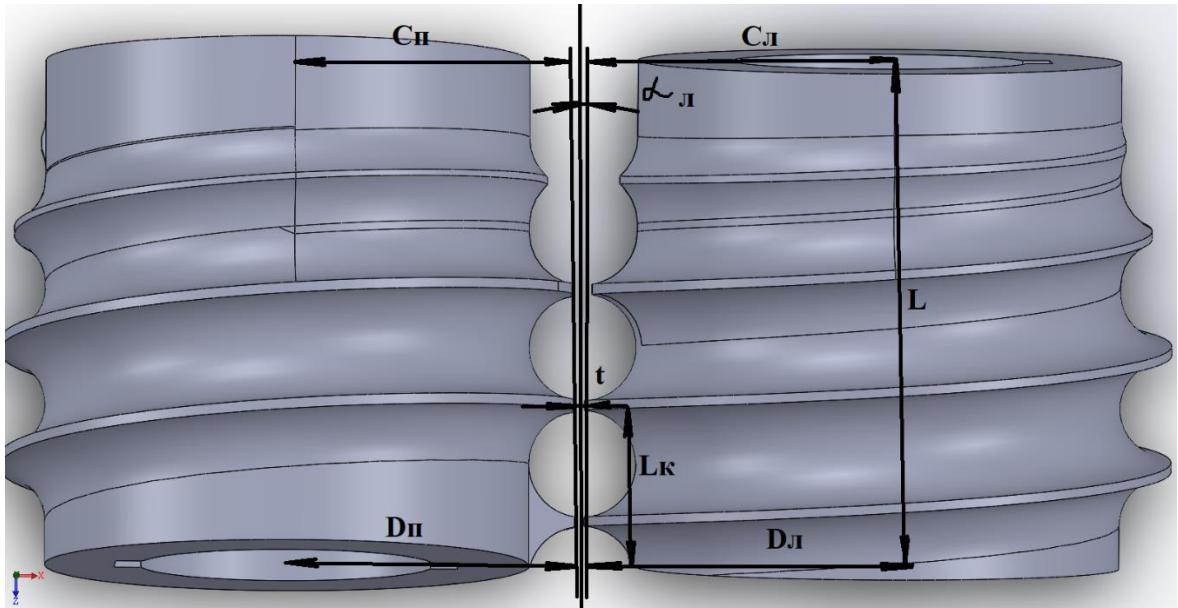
Точка скрещивания валков (вид валков сверху)
